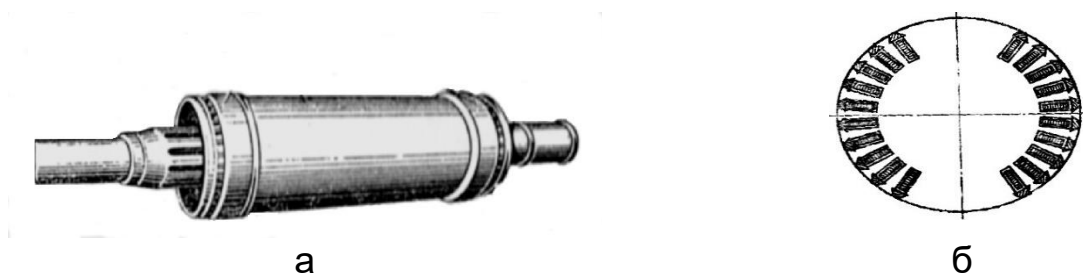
Загальний вигляд ротора турбогенератора –а та поперечний розріз ротора –б
